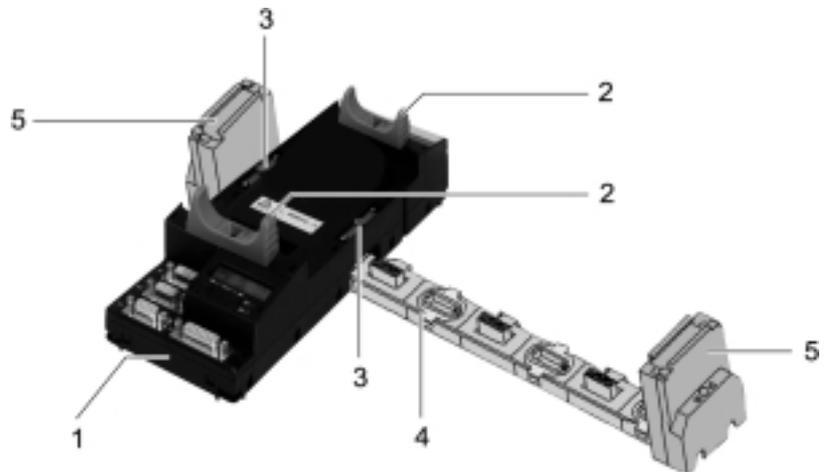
Montage des Sockels des CPU & Power Modul für Zone 1
